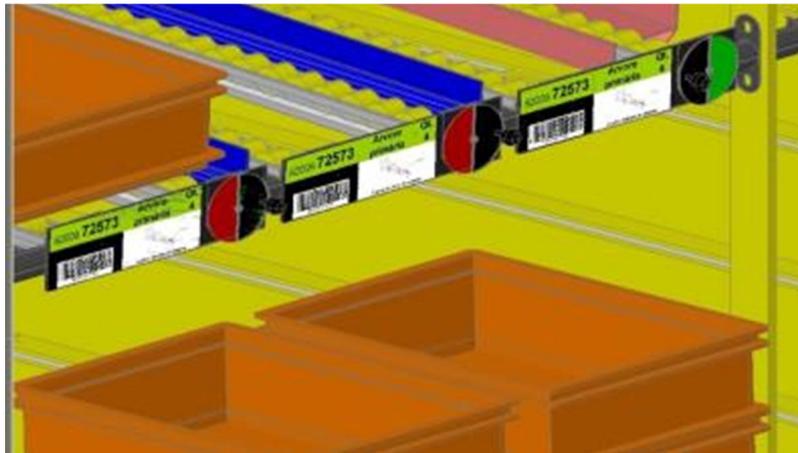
Identificação das filas com sinalização do estado (verde/vermelho)
